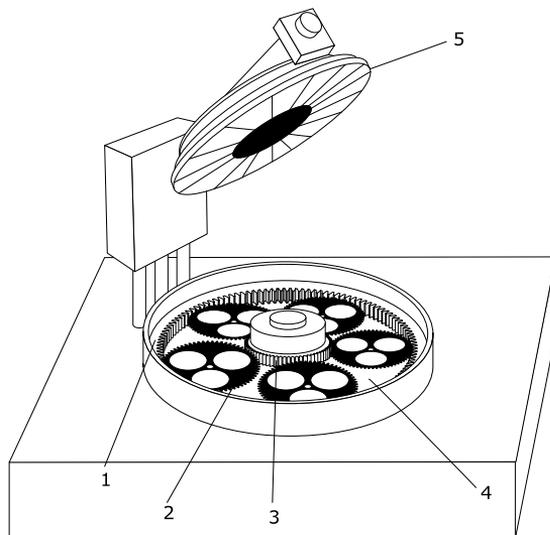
Планетарный механизм для двухстороннего шлифования пластин: 1- внешняя шестерня; 2 – сепаратор; 3 – внутренняя шестерня; 4 – нижний шлифовальный; 5 – верхний шлифовальный
